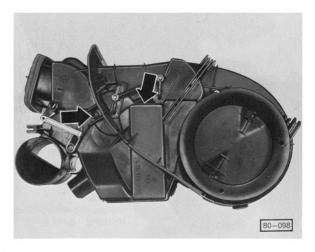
Befestigungsschrauben der linken Gehäusehälfte (Pfeile) herausdrehen
